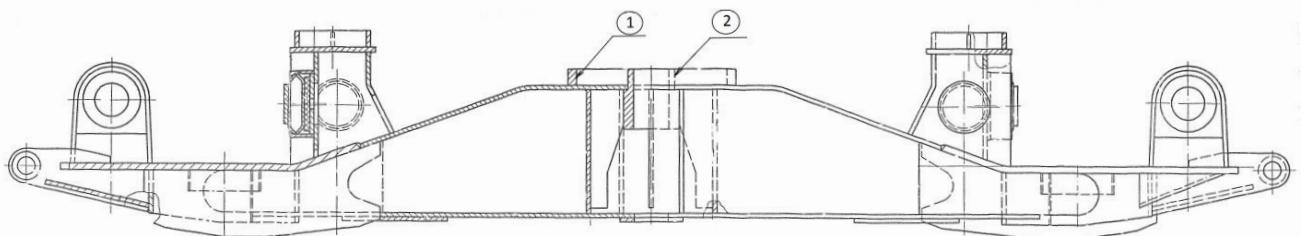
Основные дефекты балки надрессорной тележки ТВЗ-ЦНИИ-М, ремонтируемые сваркой или наплавкой
